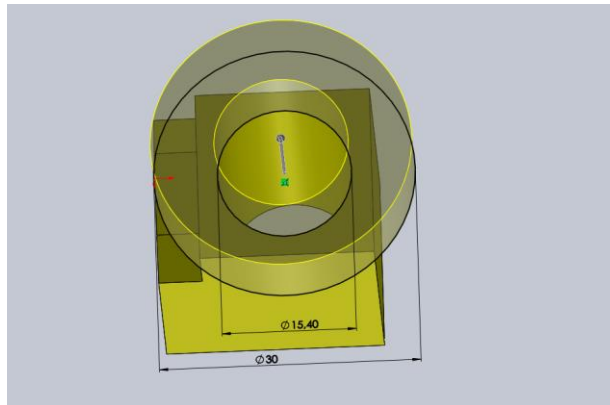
Extrusión del cilindro hasta una altura de 10mm.
